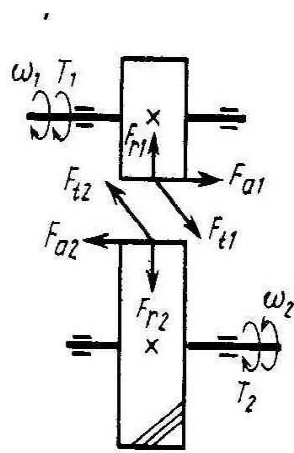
Схема сил в зацеплении косозубой цилиндрической передачи.
